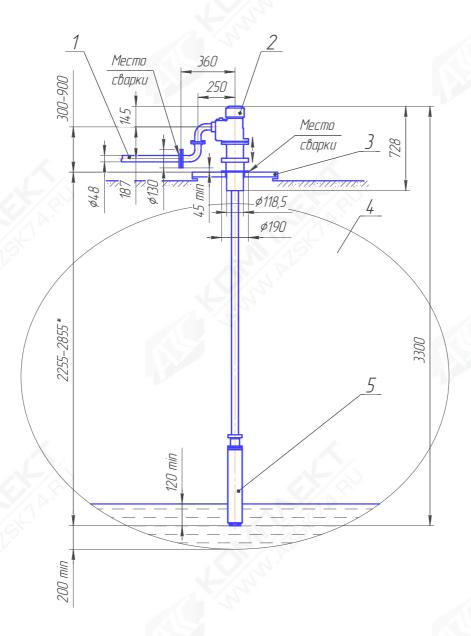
Агрегат АНП-10 исполнений 333.00.00.00-04 (-05,-06,-07,-08,-09). Состав и габаритные размеры.
